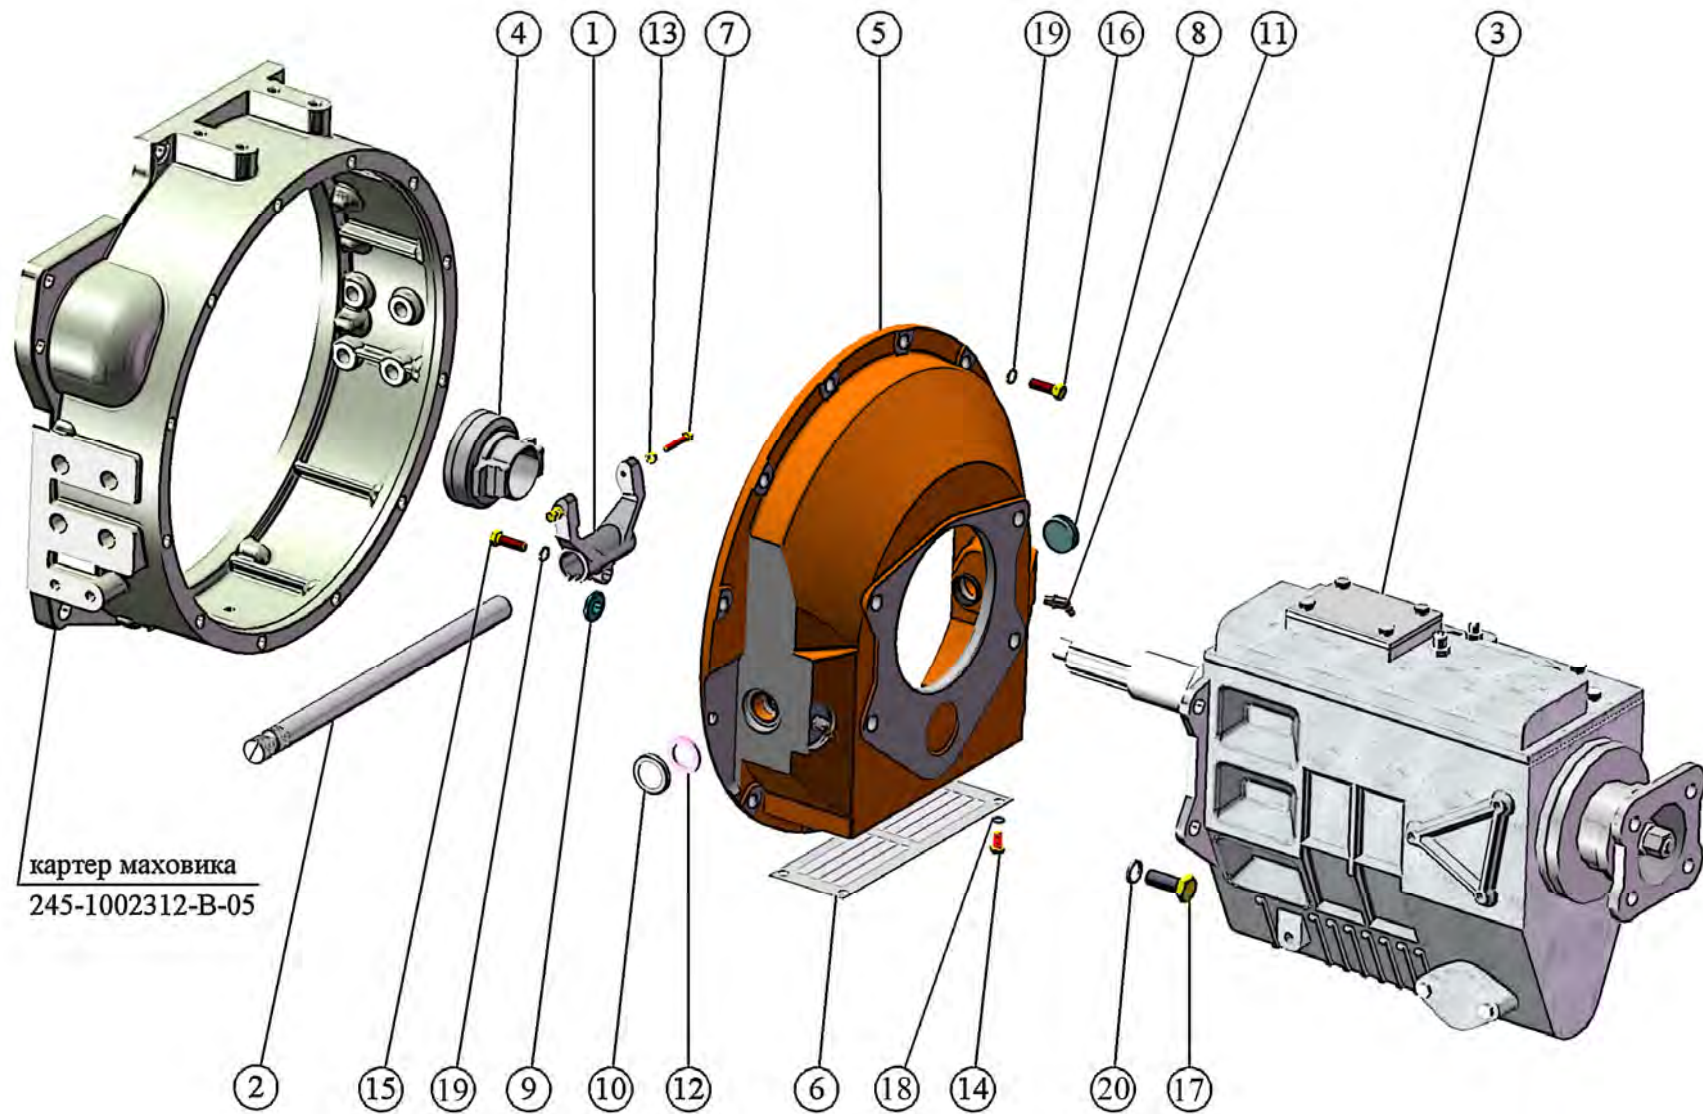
Установка картера сцепления с коробкой перемены передач.
